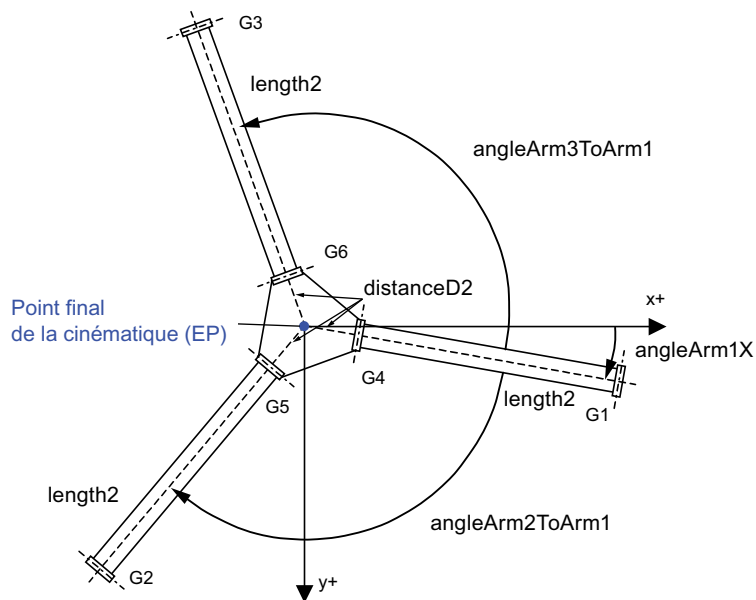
Cinématique du préhenseur delta 3D (vue d'en bas)
